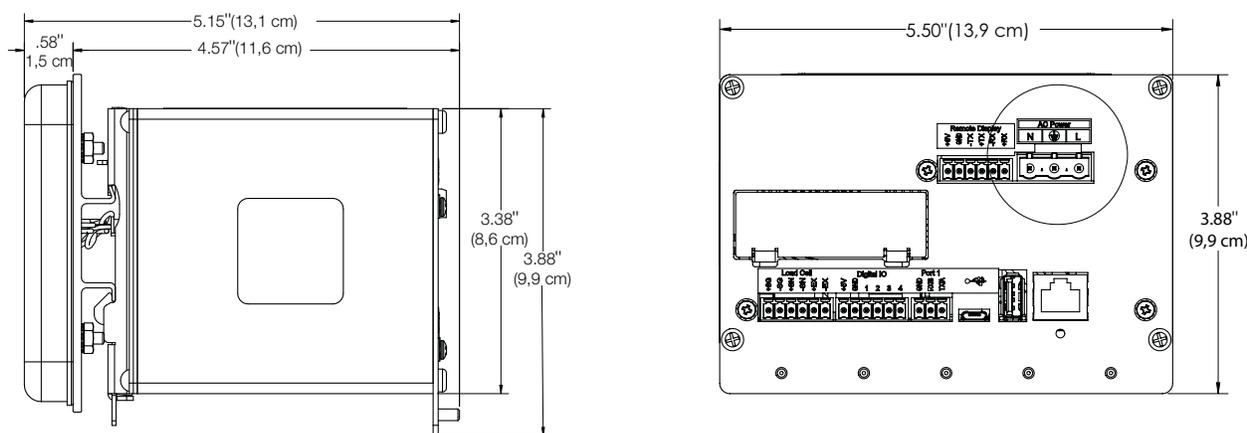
Dimensioni dell'indicatore 880 con montaggio a pannello
